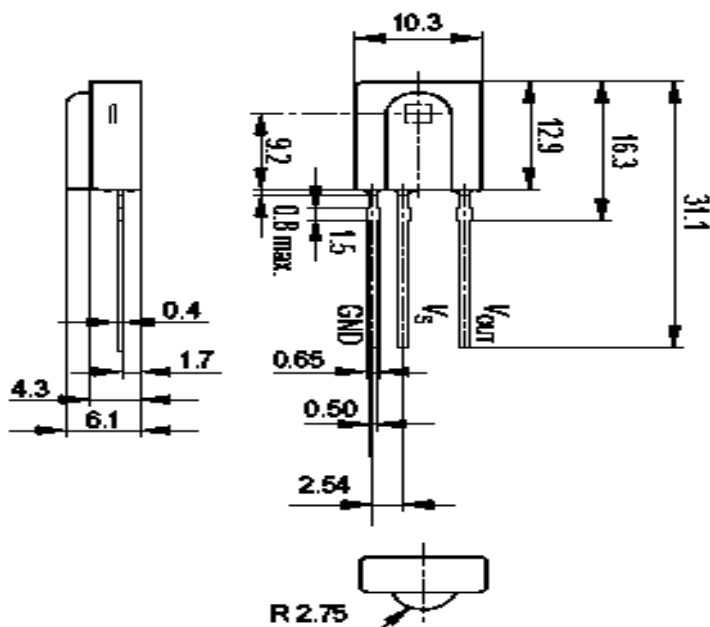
Габаритные размеры фотоприемника SFH 506
